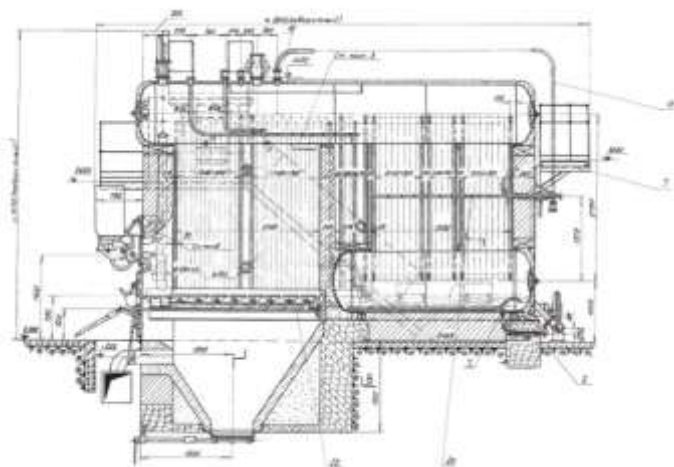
Продольный разрез и компоновка котла ДКВр6,5-13-23 с топкой ПМЗ-РПК-2 2600/2440, [2]
